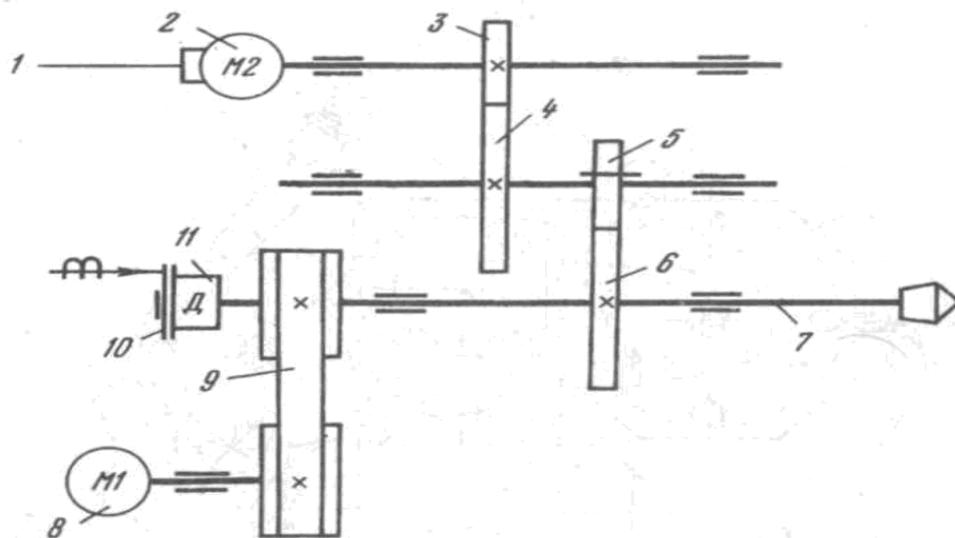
Двухдвигательный привод шпинделя со скользящей шестерней.
